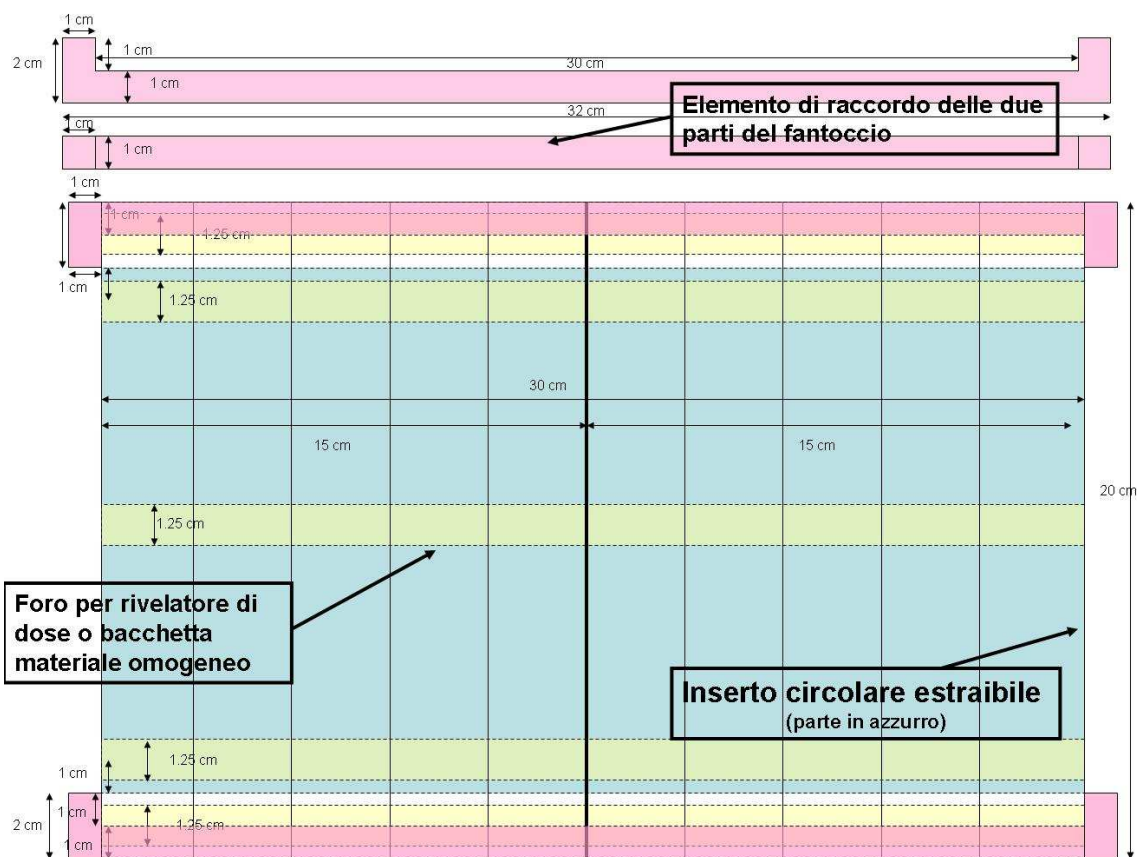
Sezione trasversale dell'oggetto test CTDI OVALE
